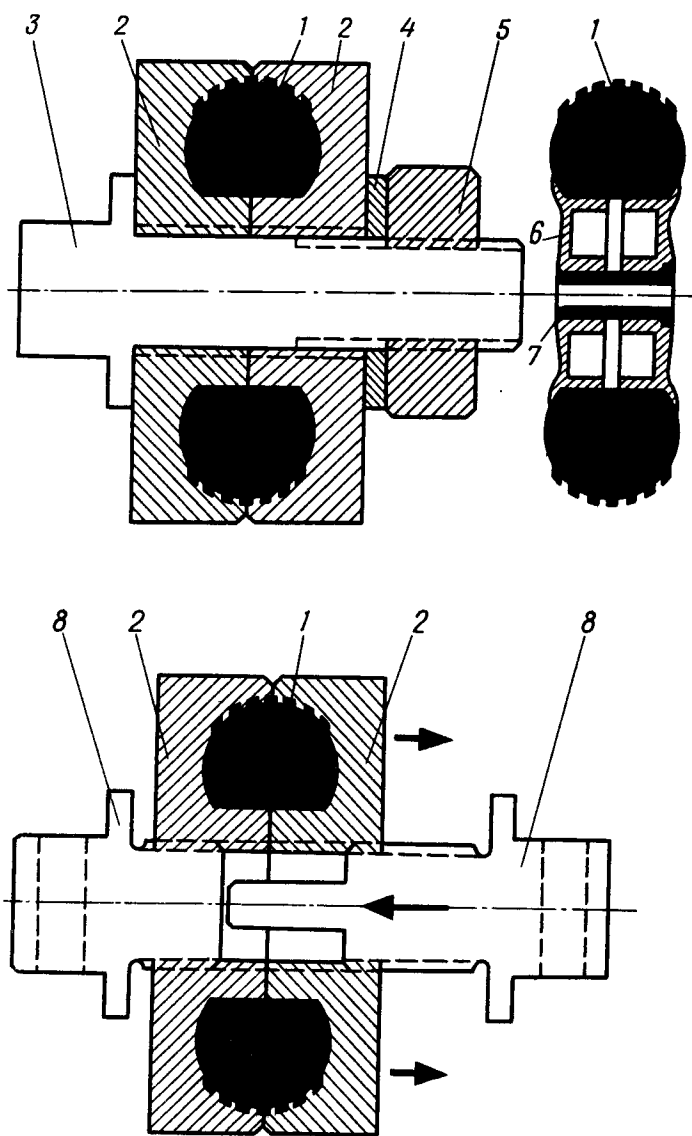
Пресс-форма колеса макета, колесо в сборе и разъемник:
